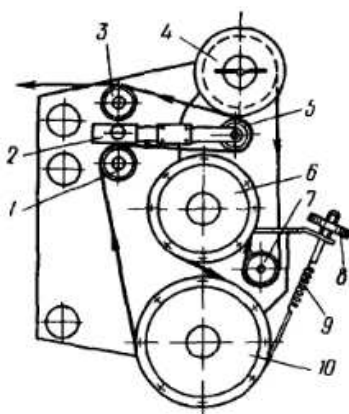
Кинематическая схема каретки бандажировочного станка с механизмом натяжения
